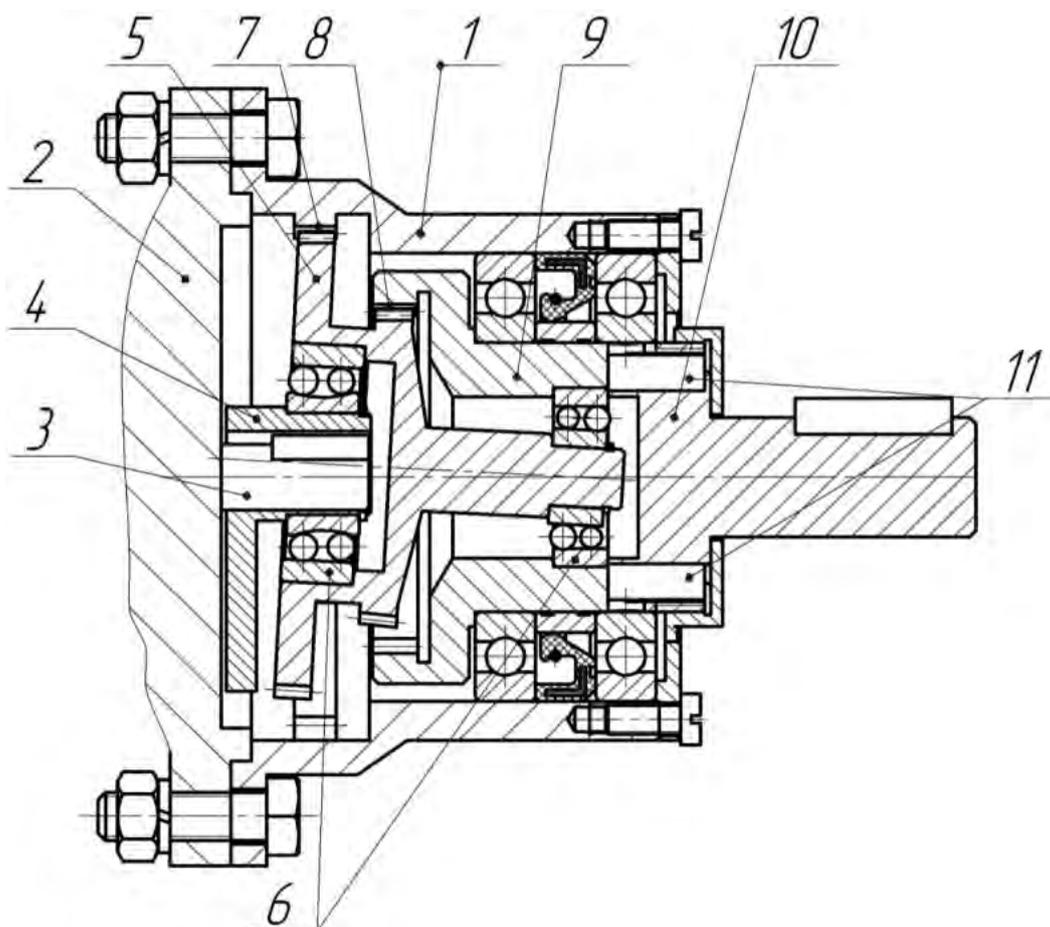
Общий вид мотор-редуктора, разработанного на основе прецессионной передачи типа 2К-Н: 1 – корпус; 2 – фланец электродвигателя; 3 – выходной вал электродвигателя; 4 – эксцентриковая втулка с противовесом; 5 – сателлит; 6 – сферические подшипники; 7, 8 – зубчатый венец; 9 – промежуточный вал; 10 – выходной вал; 11 – призматические шпонки
